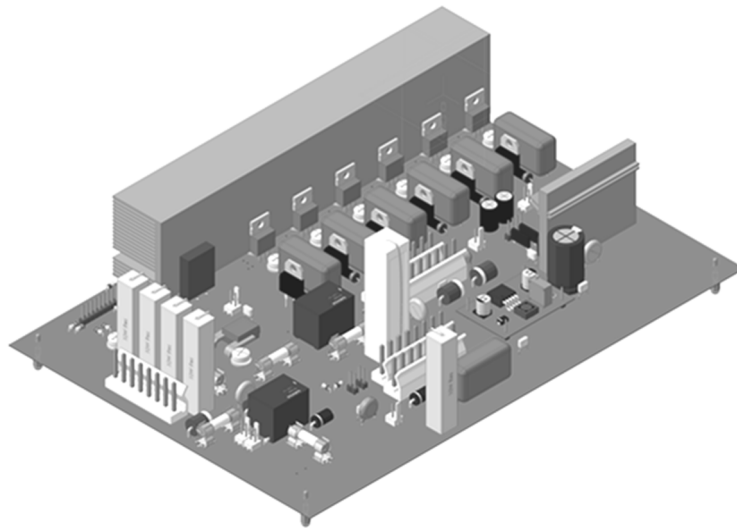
3D-модель плати системи керування приводу електромобіля
